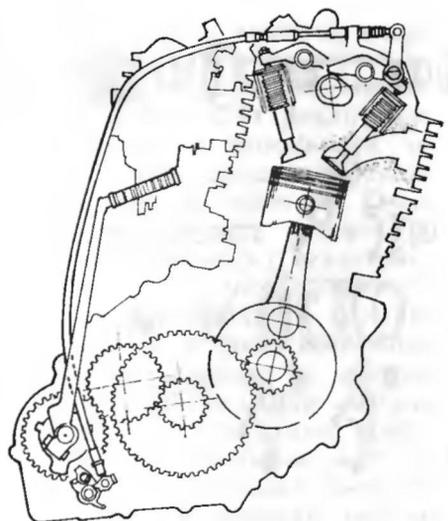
Система пуска четырехтактного двигателя «Ямаха ХТ 550». Выпускной клапан автоматически открывается при начале движения пускового рычага управления
